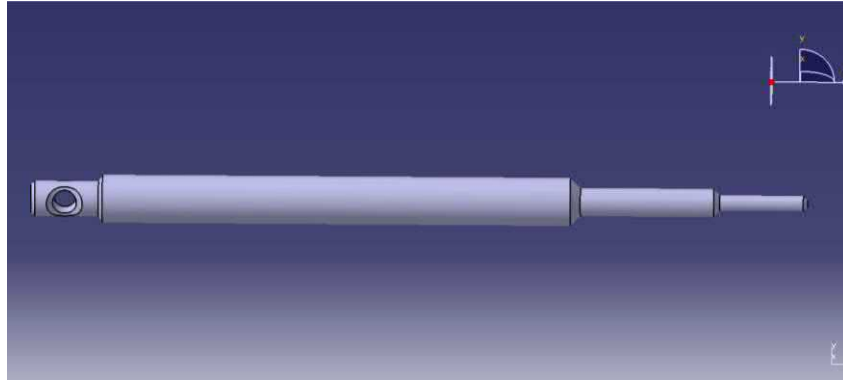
Desain Lengkap *Inner Puller Bearing 2
